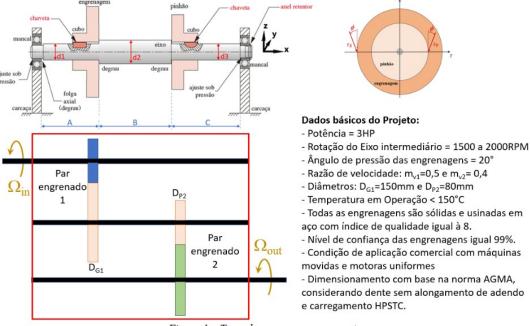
Trem de engrenagem composto. Dimensões: A=50mm; B=100mm; C=50mm.
